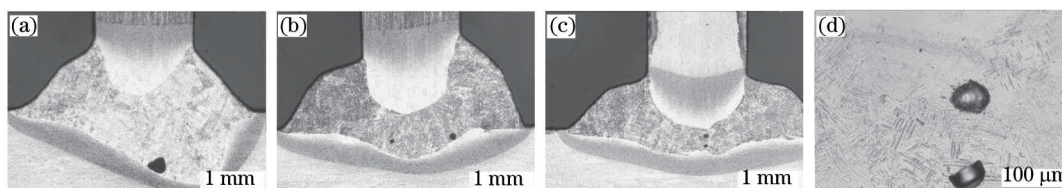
不同焊接参数下焊缝中气孔的形貌:(a) 2800 W, 6 m/min;(b) 1400 W, 3 m/min;(c) 1400 W, 4 m/min;(d)图(c)中气孔局部放大
